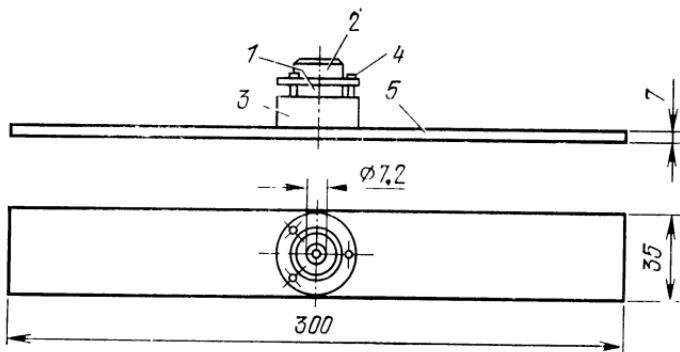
Индикатор уровня для диска проигрывателя:
